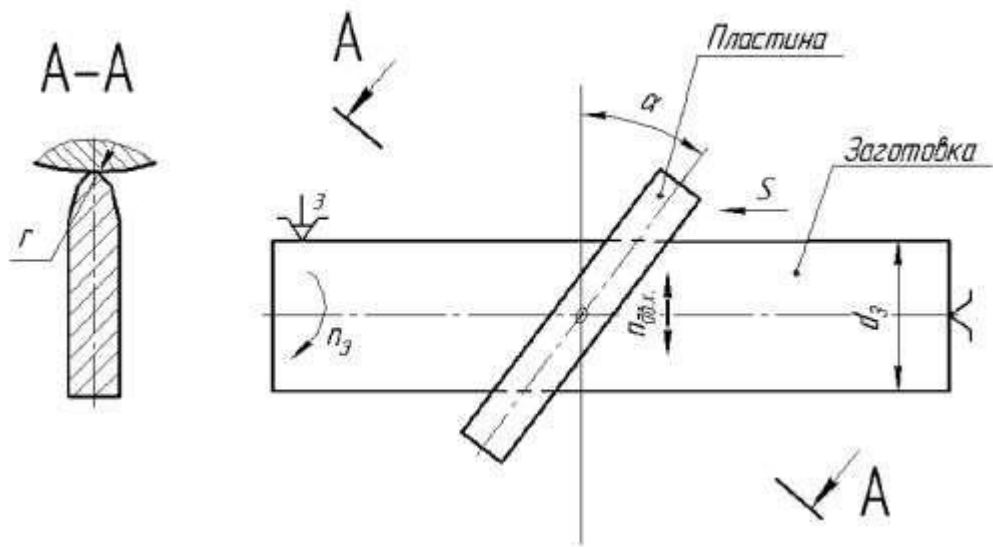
Схематичне зображення коливального процесу згладжування циліндричних деталей.
